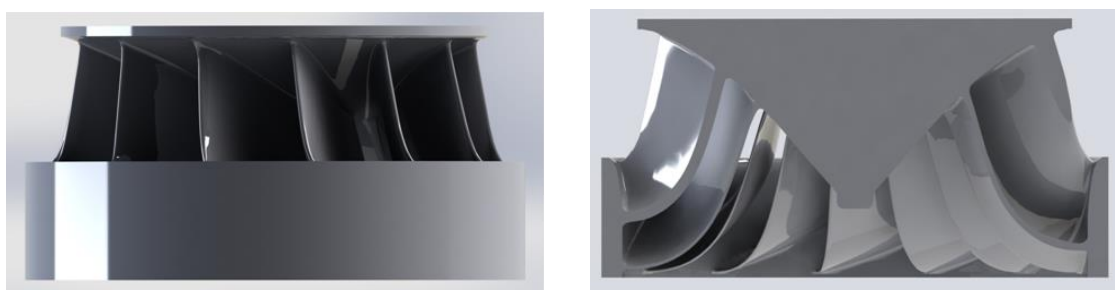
MODELAGEM 3D DA RODA ESCANEADA A) VISTA; B) CORTE LONGITUDINAL
